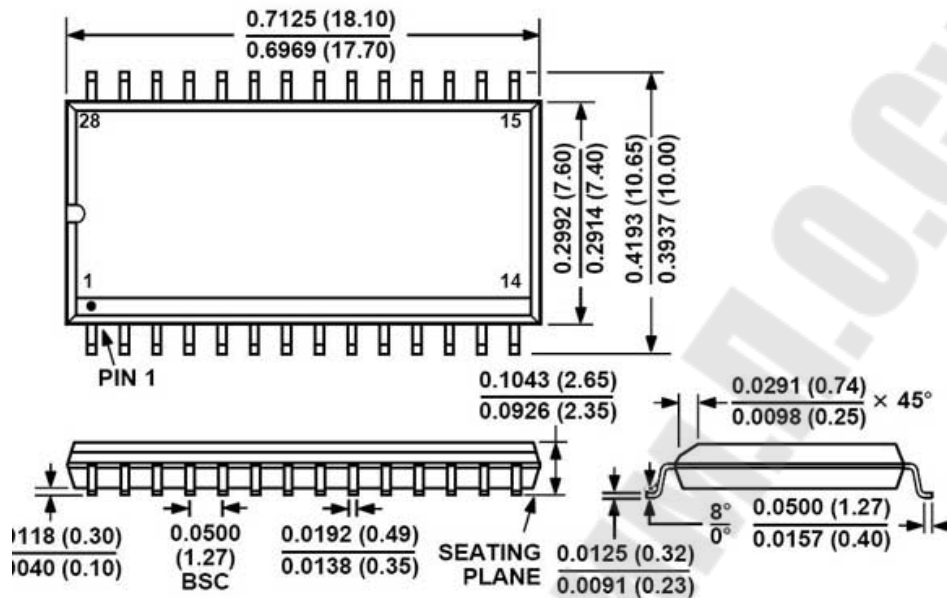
Геометрические размеры корпуса SOIC-28
